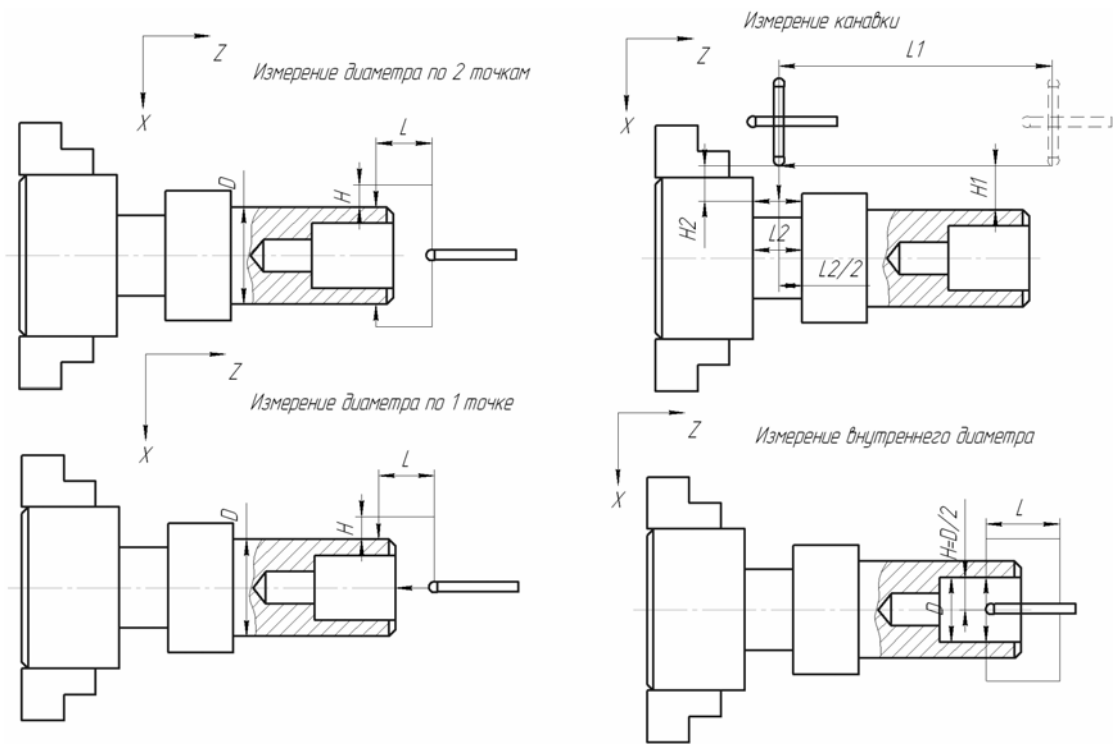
Циклы измерения вала на токарном станке с ЧПУ 1В340Ф30
